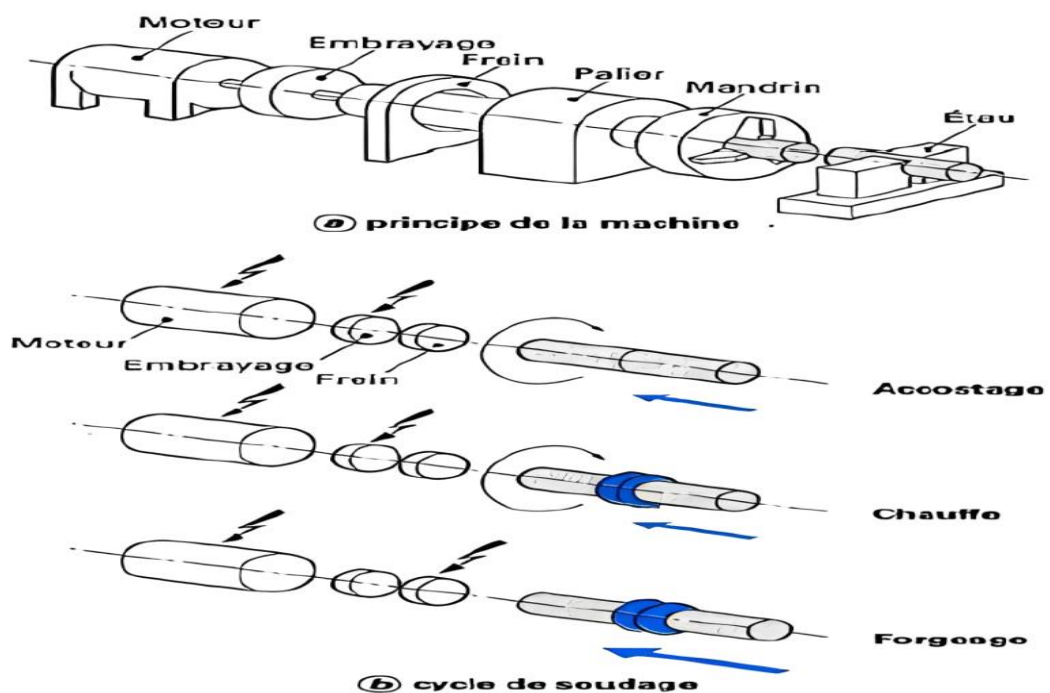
Soudage par entraînement direct ou continu [27].
